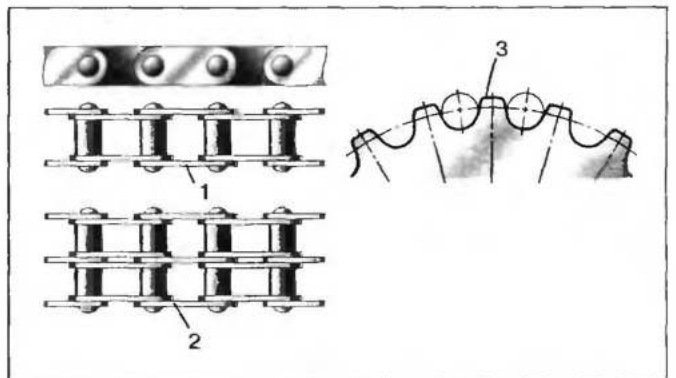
Роликовая цепь привода распределительного вала: 1 — однорядная; 2 — двухрядная; 3 — звездочка привода
